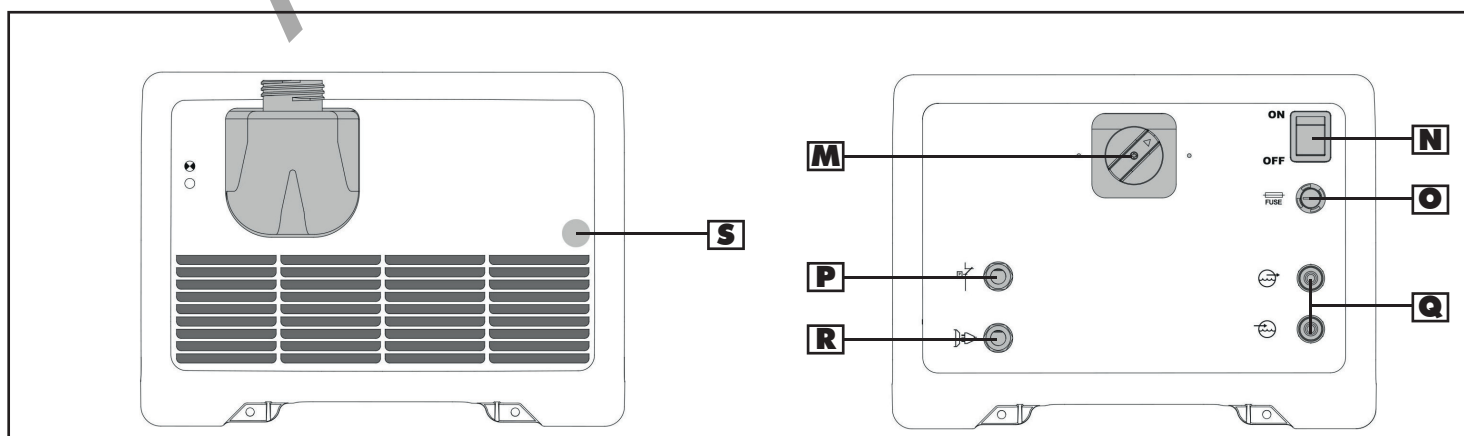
Вид передней и задней панелей блока охлаждения для сварочного инвертора с внешним устройством подачи проволоки
